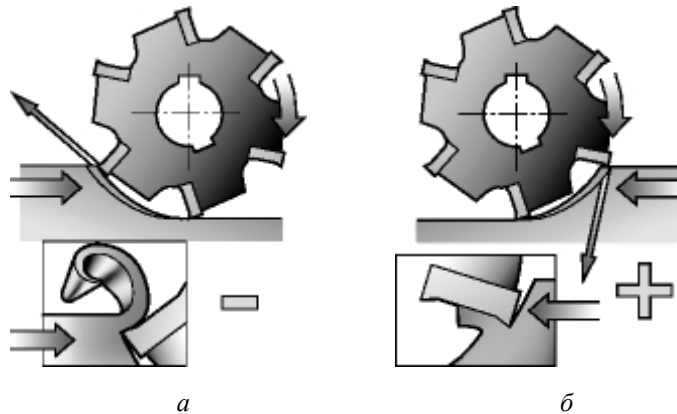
Схема зустрічного (а) та попутного (б) фрезерування
